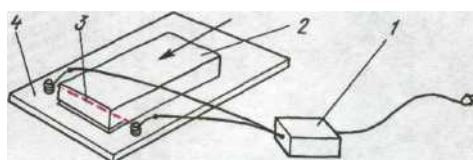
Прибор для резки пенопласта: 1 — прибор; 2 — пенопласт; 3 — проволока-нагреватель; 4 — доска
